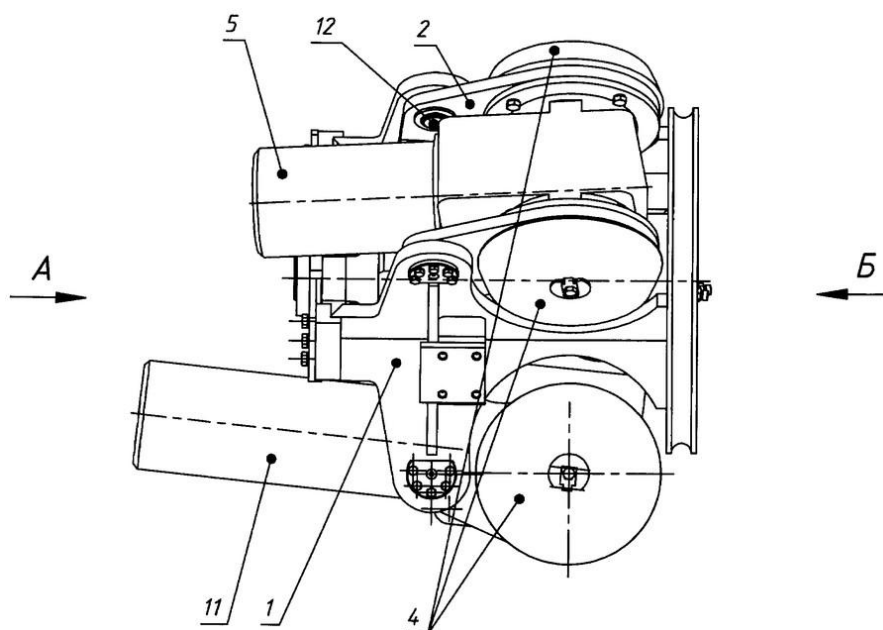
Механизм перемещения машины для сварки труб, в дальнейшем "механизм перемещения", вид спереди
